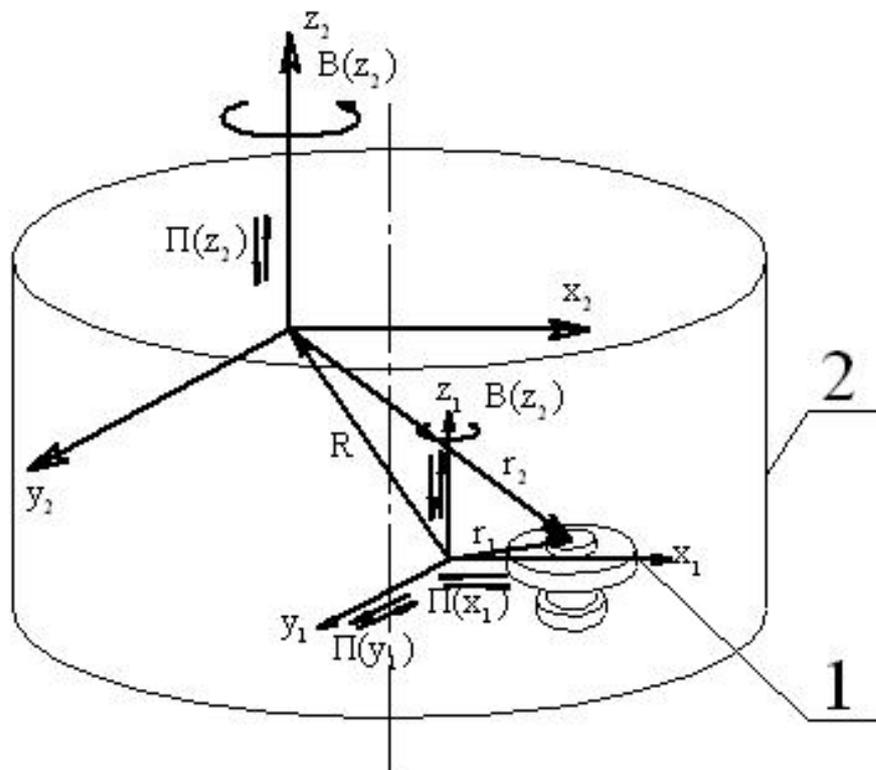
Кинематическая схема процесса обработки зубчатого колеса предлагаемым способом
